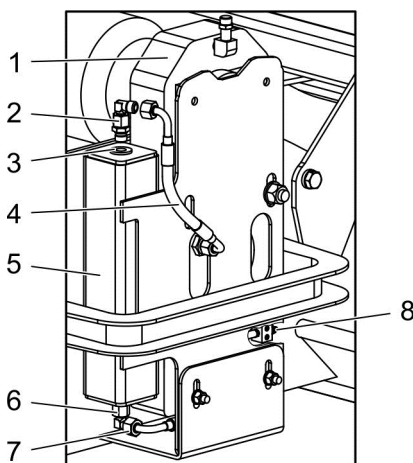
ТО центрального редуктора снегоуплотнительного оборудования МСУ-622
